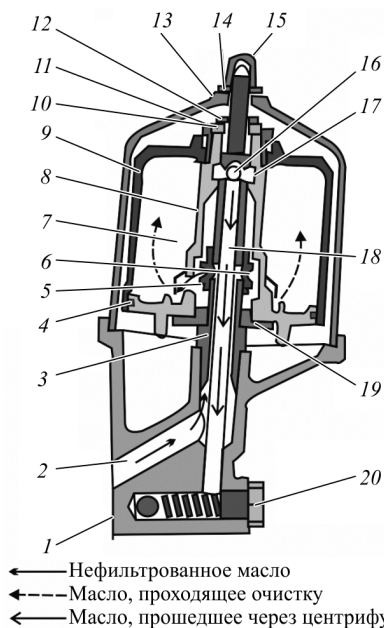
Реактивная центрифуга дизеля Д-240: 1 – корпус центрифуги; 2 – подводный канал; 3 – ось ротора; 4 – резиновое кольцо; 5 – выходные отверстия; 6 – насадка; 7 – внутренний стакан; 8 – остов ротора; 9 – верхняя крышка ротора; 10 – гайка специальная; 11, 14 – шайбы; 12 – гайка; 13 – колпак; 15 – колпачковая гайка; 16 – тангенциальные отверстия; 17 – радиальные отверстия; 18 – маслоотводящая трубка; 19 – нижняя крышка ротора; 20 – сливной клапан
